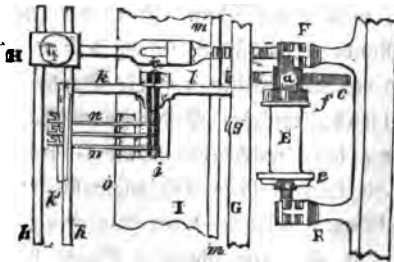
Mechanismus der Seidendoublirmachine. — Grundriß.
